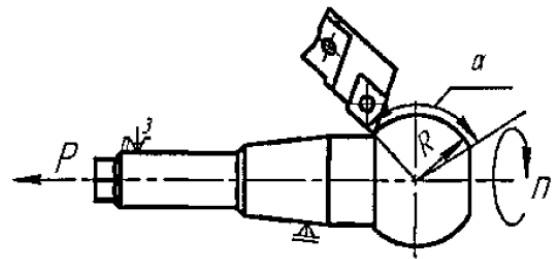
Схема токарної обробки сфери кульового пальця з використанням поворотного пристрою
